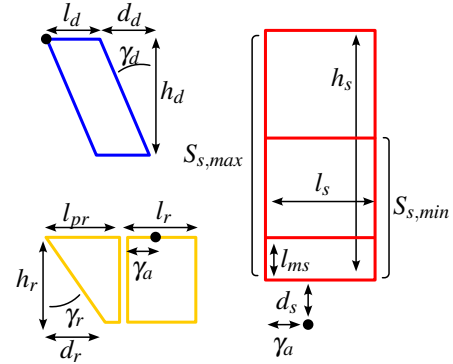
Dimensionnement particulier de 3 sous-ensembles.
